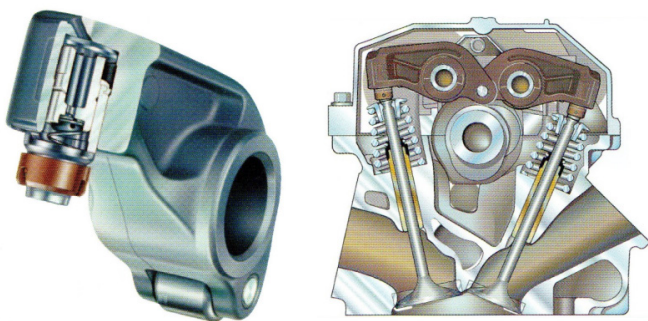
Гидравлический компенсатор, установленный в коромысле привода клапана, получает масло из оси коромысла; источник: *Schäffler Gruppe Automotive*.
